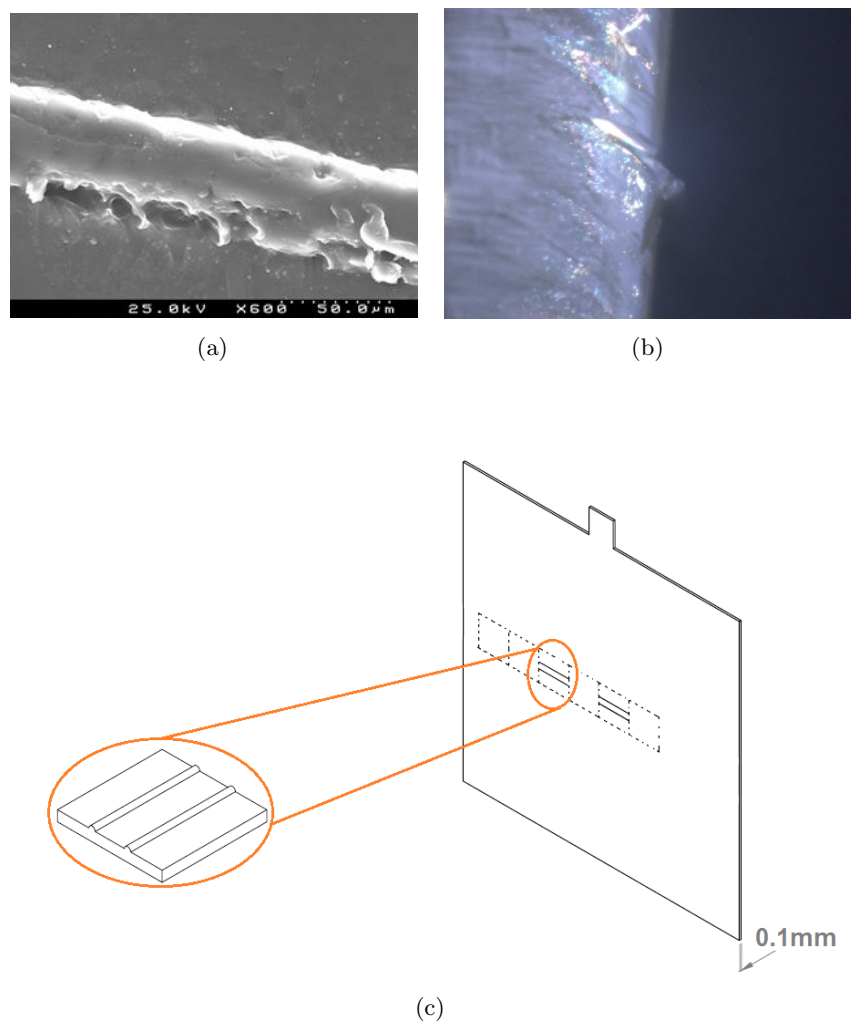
(a) Superfície da peça moldada; (b) secção transversal da peça moldada e (c) esquema das peças moldadas obtidas.
